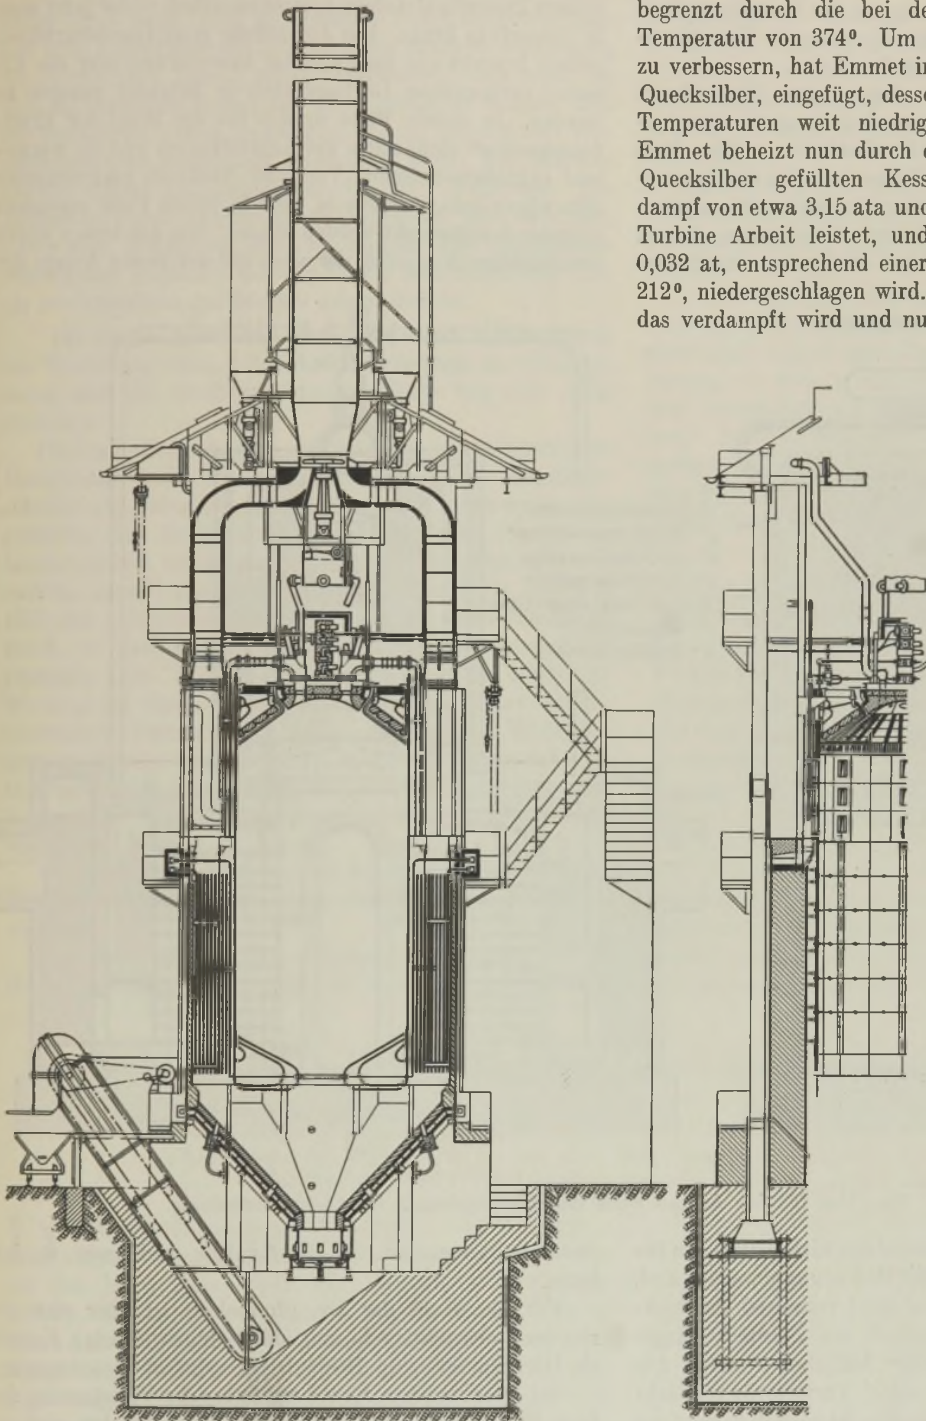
Benson-Kessel für Kohlenstaubfeuerung.
